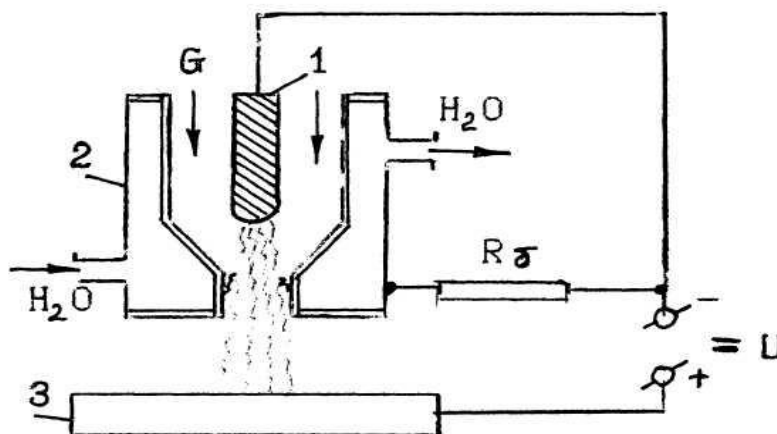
Схема плазменного нагрева детали с помощью ЭДП: 1-катод ЭДП; 2- сопло, анод; 3- деталь; R- балластное сопротивление; G- поток газа.
